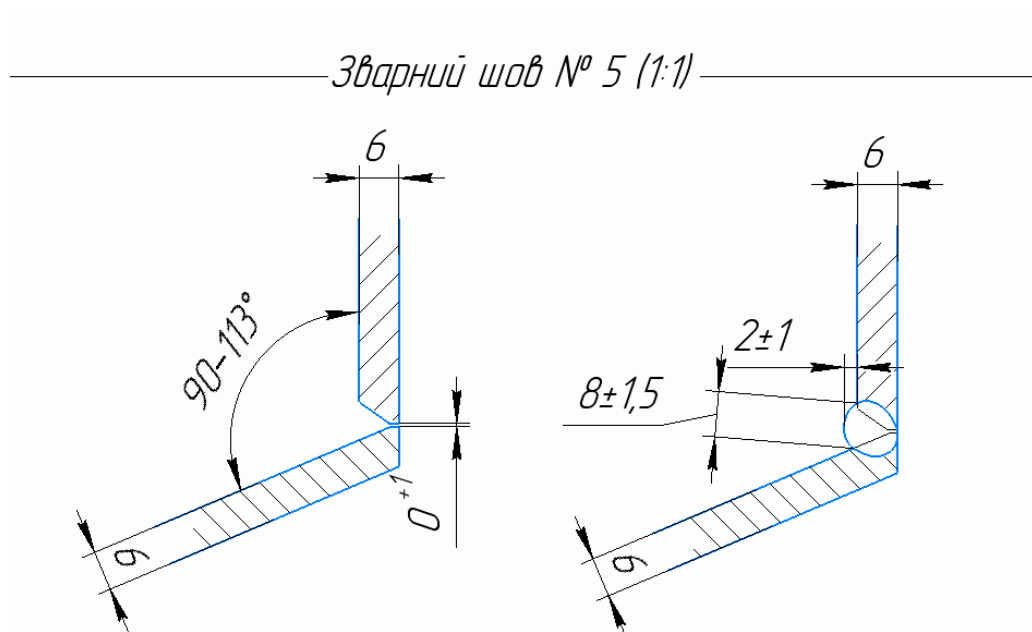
Схема підготовки до зварювання та зварного шву №5
